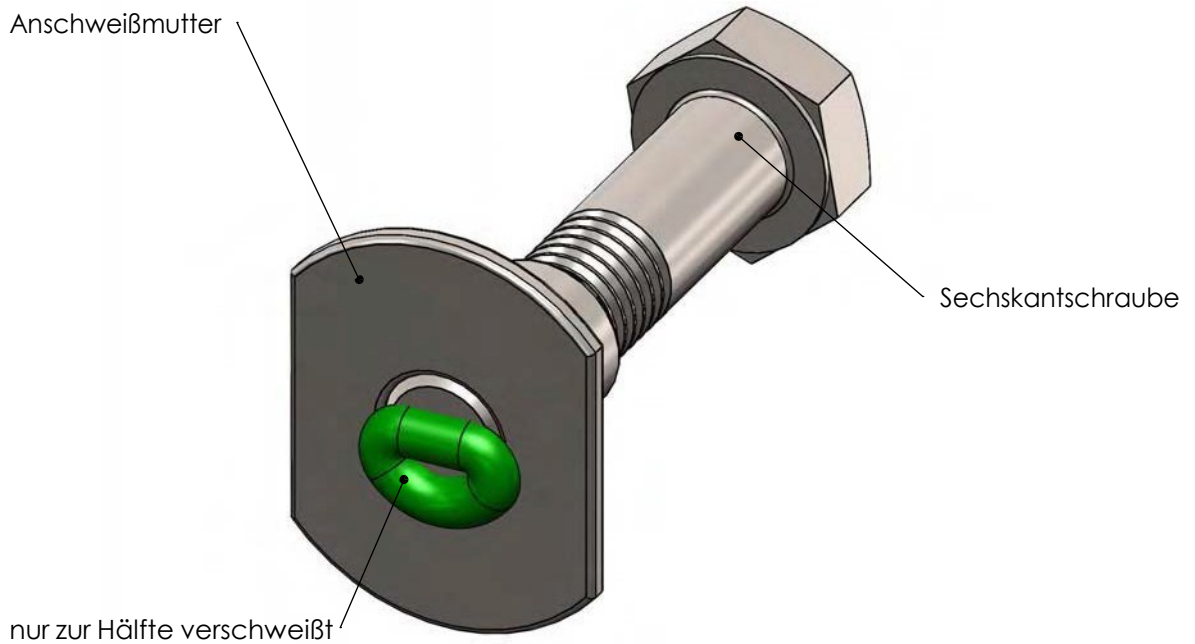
Beispiel einer inneren Verschweißung
